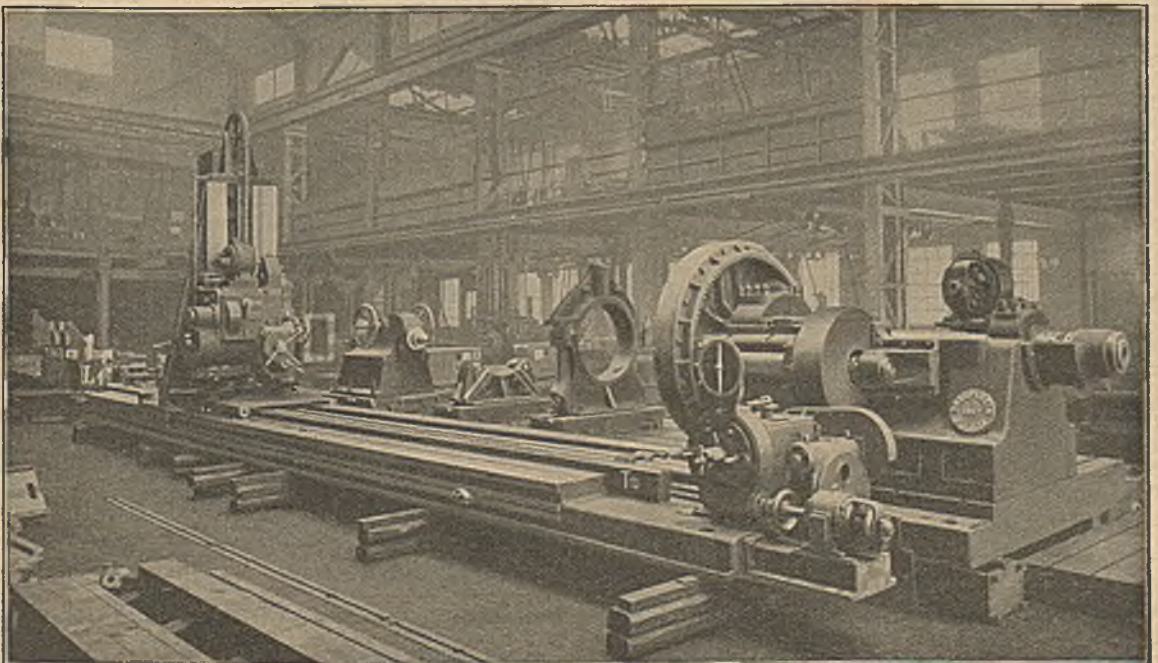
Schwere Zahnradfräsmaschine von Droop & Rein.
